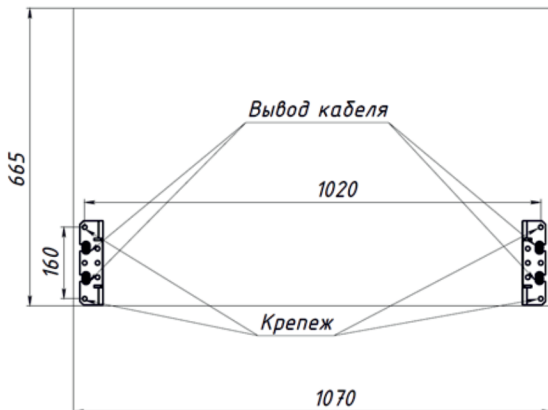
Размеры и назначение отверстий каблучков турникета
